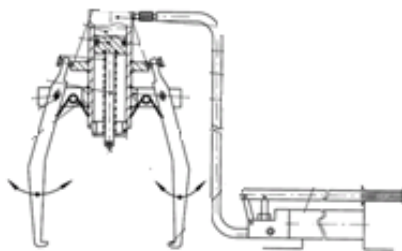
Съёмник гидравлический для демонтажа деталей
